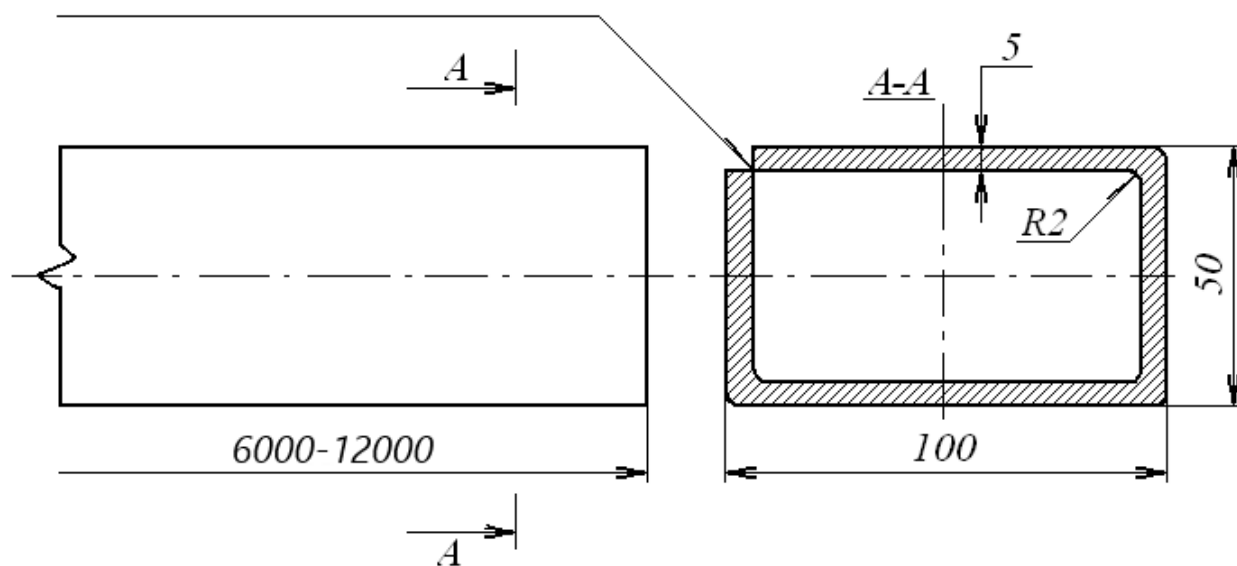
Конструкція електрозварної прямокутної труби
